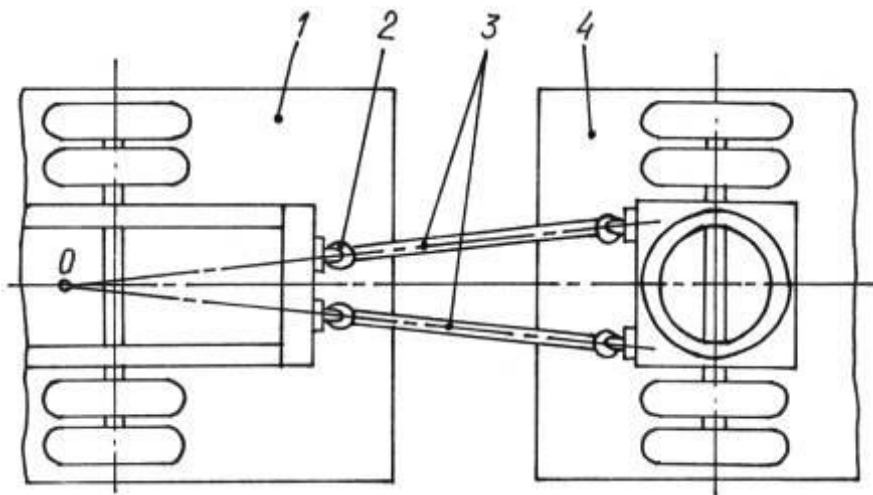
Схема поворотно-зчіпного чотирьохланкового механізму:
